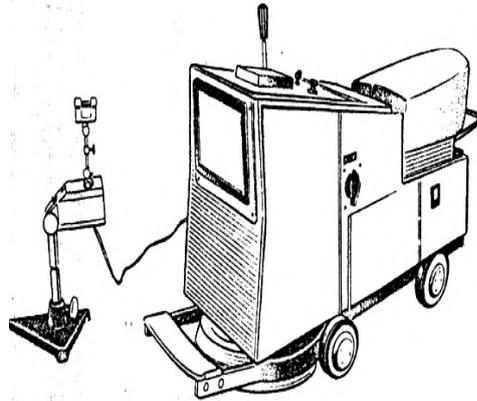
Станок К-125 для балансировки колес на автомобиле
